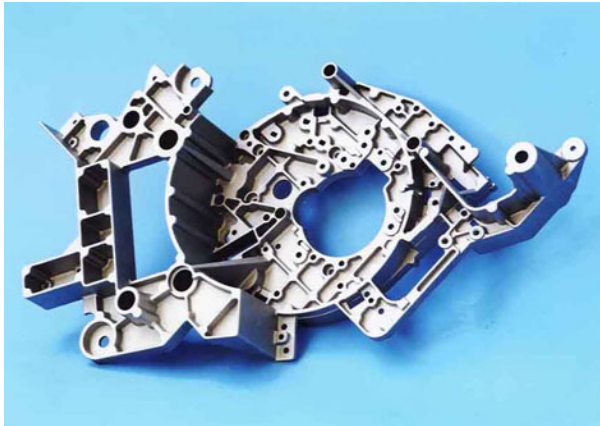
rfZ) Moderner Aluminium Druckguss (Druckguss Waghäusel)
